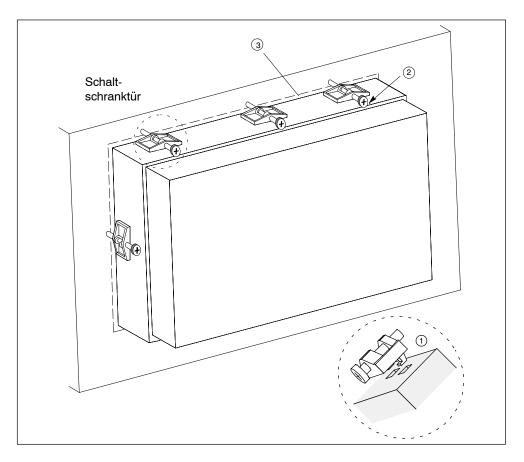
Mechanische Befestigung des C7-635 Touch
